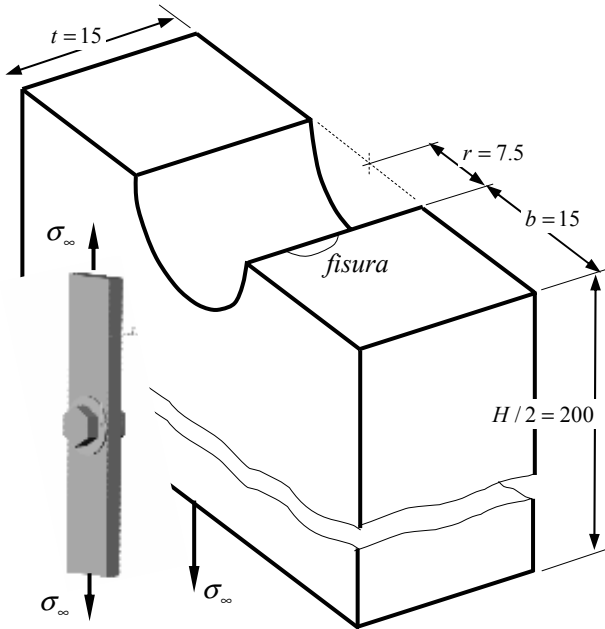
Dimensiones (en mm) de la chapa sobre la que se montará la unión.
